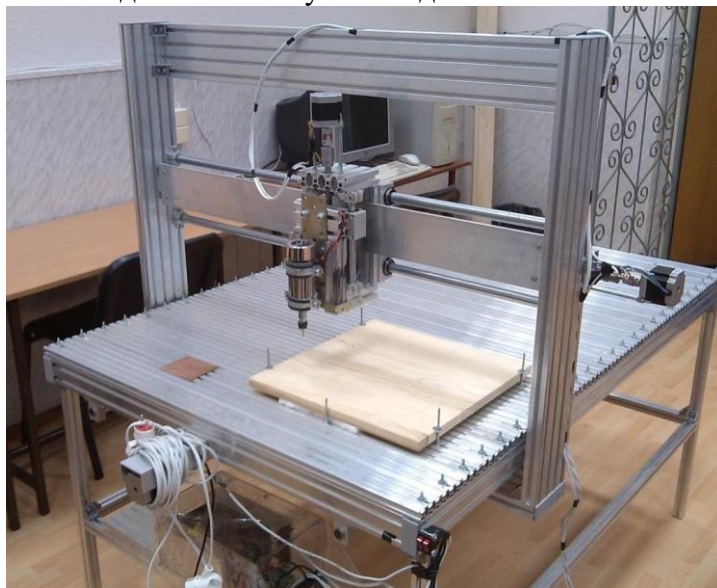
Фрезерний станок з ЧПК, який створений студентами кафедри КІТВТ для різьби по дереву
